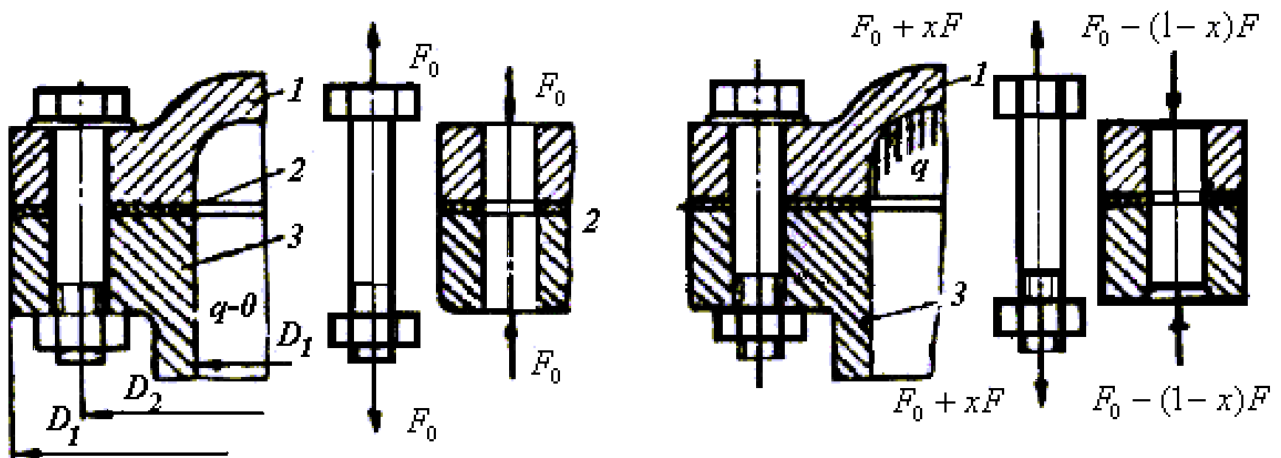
Резьбовое соединение с затянутым болтом: 1 – крышка, 2 – прокладка, 3 – цилиндрический корпус
